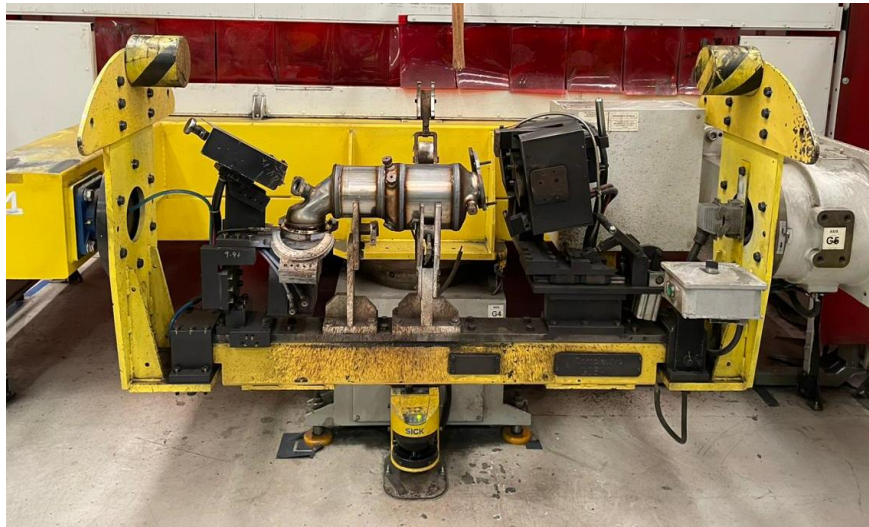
Pieza soldada terminando ciclo de soldadura. Fuente. elaboración propia
